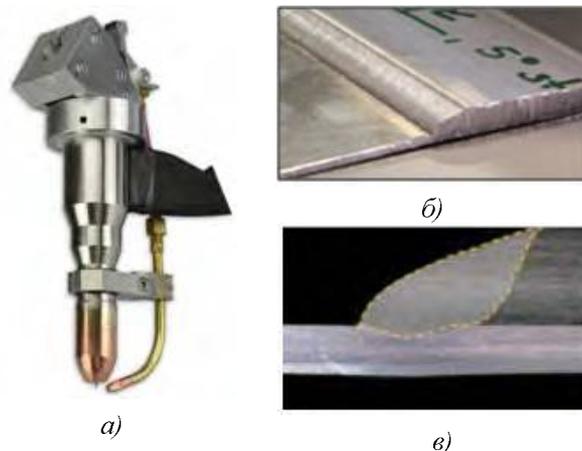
Оборудование для плазменной сварки: а – сварочная головка Kjellberg; б – послойная сварка изделия; в – сечение сварочного шва (информация с сайта www.kjellberg.de)
